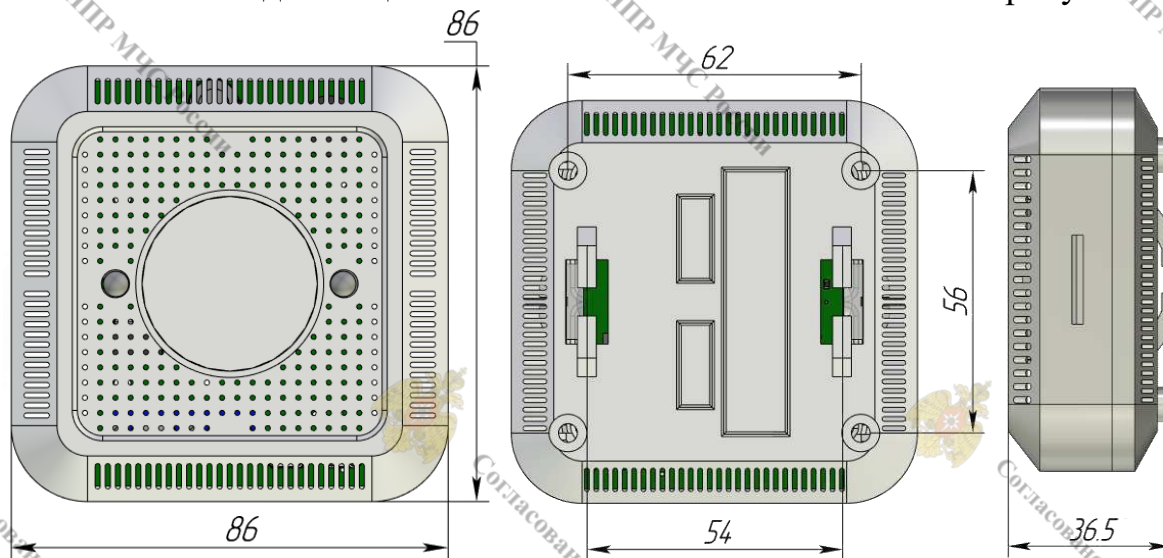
Внешний вид извещателя газового «ИП 435-1»
